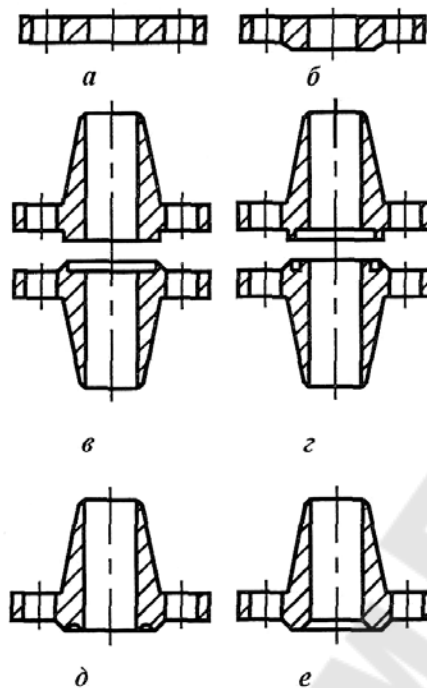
Уплотнительные поверхности фланцев: а – без выступов; б - с соединительным выступом; в - с выступом и впадиной; г - с шипом и пазом; д - под прокладку овального сечения; е - под линзовую прокладку
